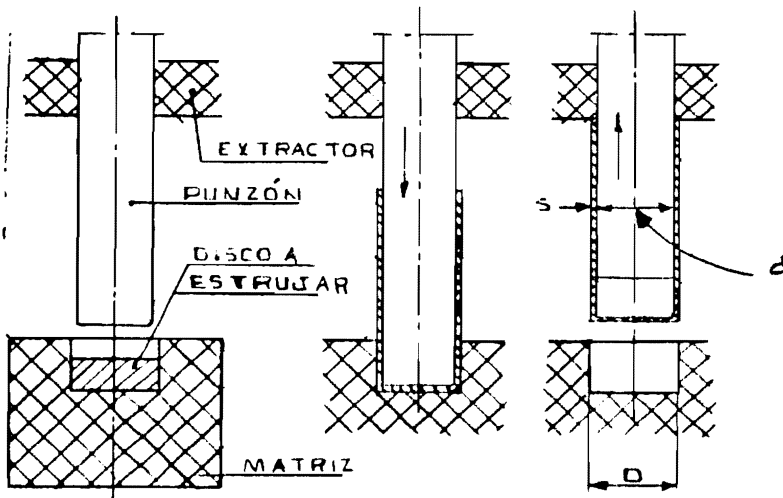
Proceso de extrusión, en el que se muestra el flujo del metal.
